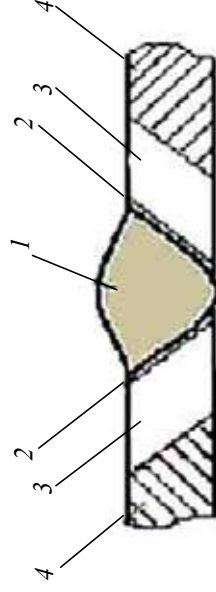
Строение стыкового сварного соединения:
